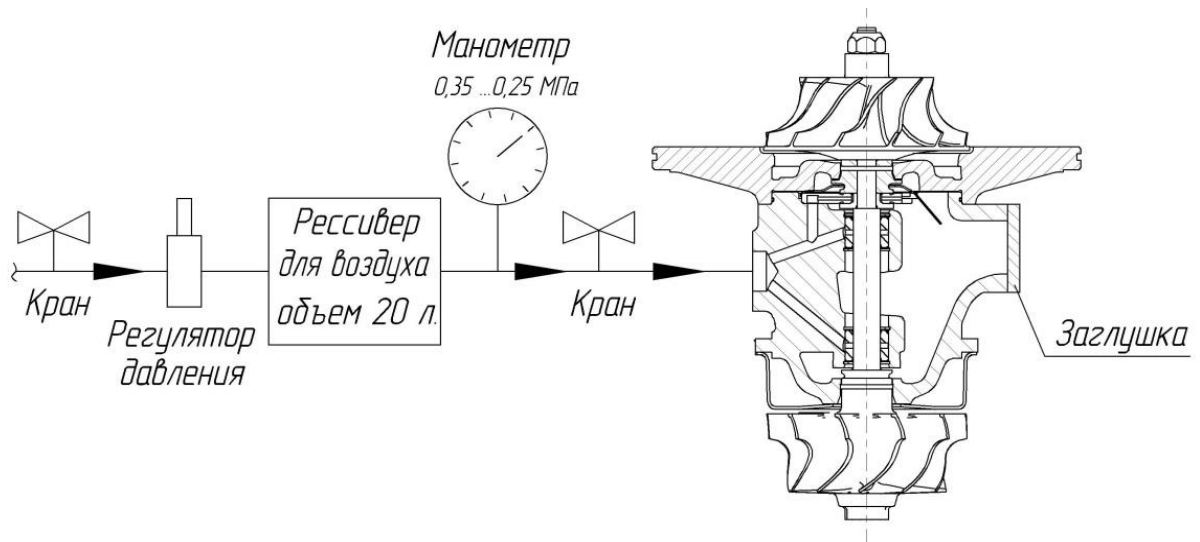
Схема установки для проверки герметичности подшипникового узла с ротором турбокомпрессора
